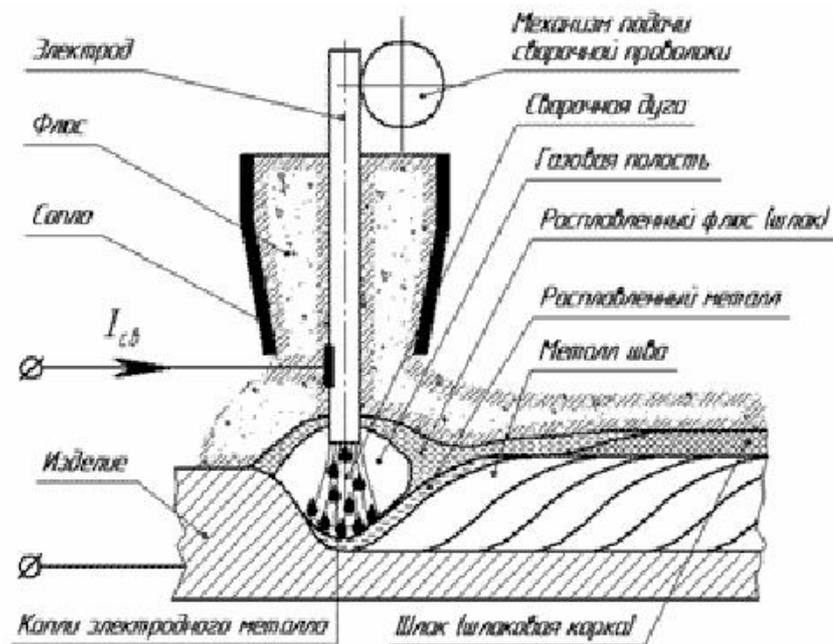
Схема сварки под слоем флюса
